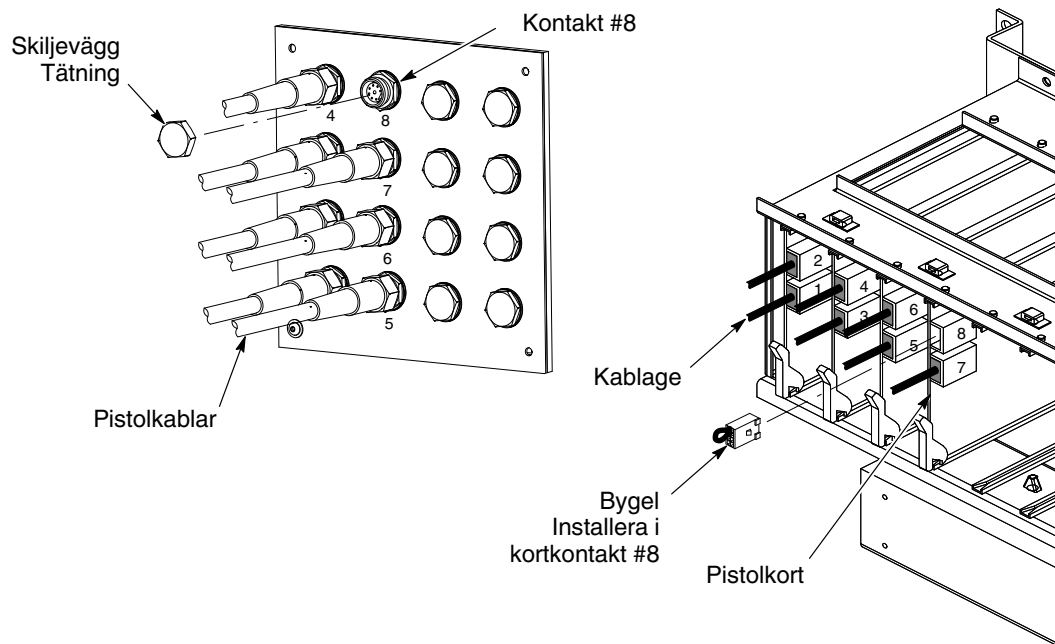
Installation av plugg och bygling - exempel med 8-pistolers system med 7 pistoler
